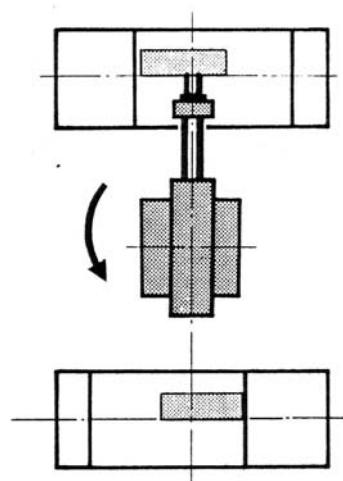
Robot pneumatic pentru transferul piesei de la o masina la alta
